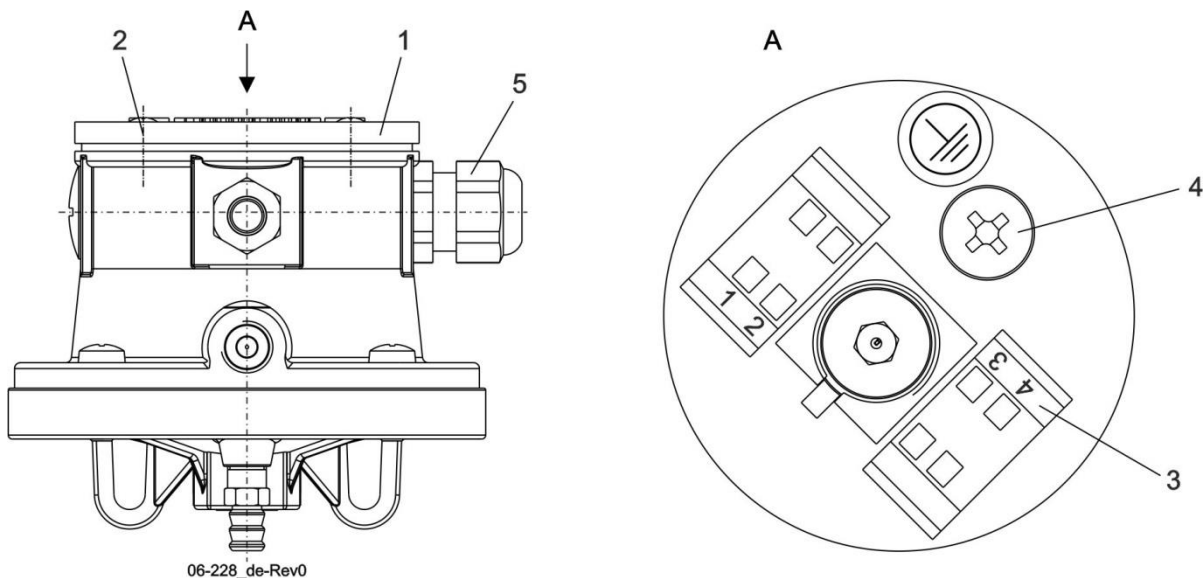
Klemmenbelegung bei Kabelanschluss (Draufsicht auf Anschlussklemmen und Erdungsschraube)
